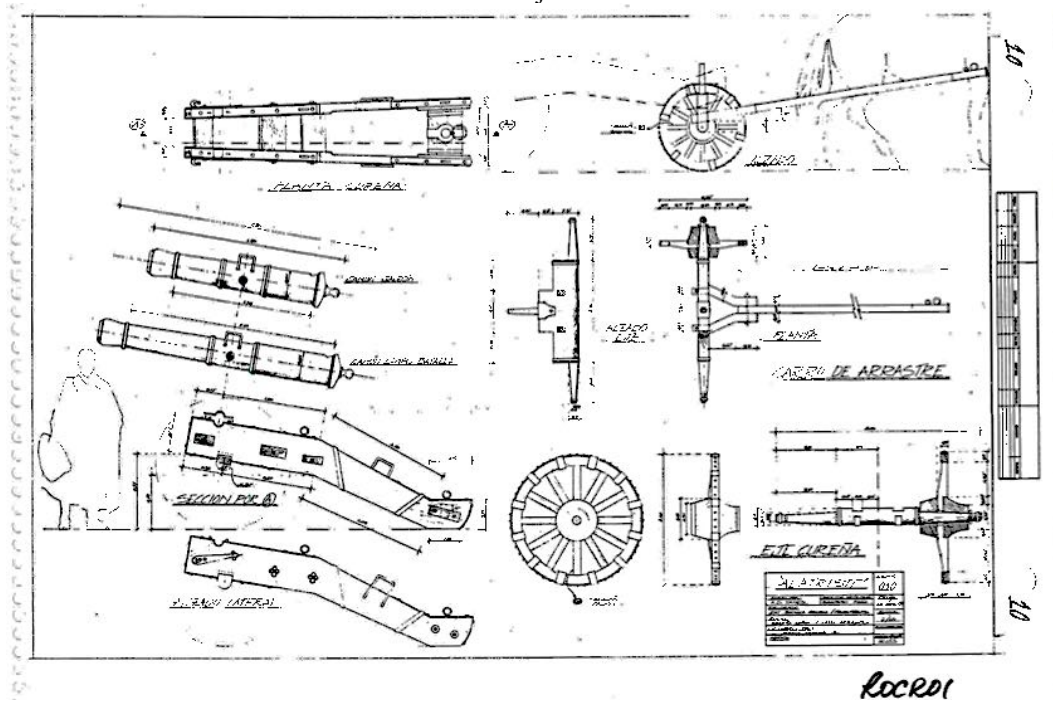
Plano. Planta y alzado cureña y carro de arrastre de cañones. *Alatrisme*.
